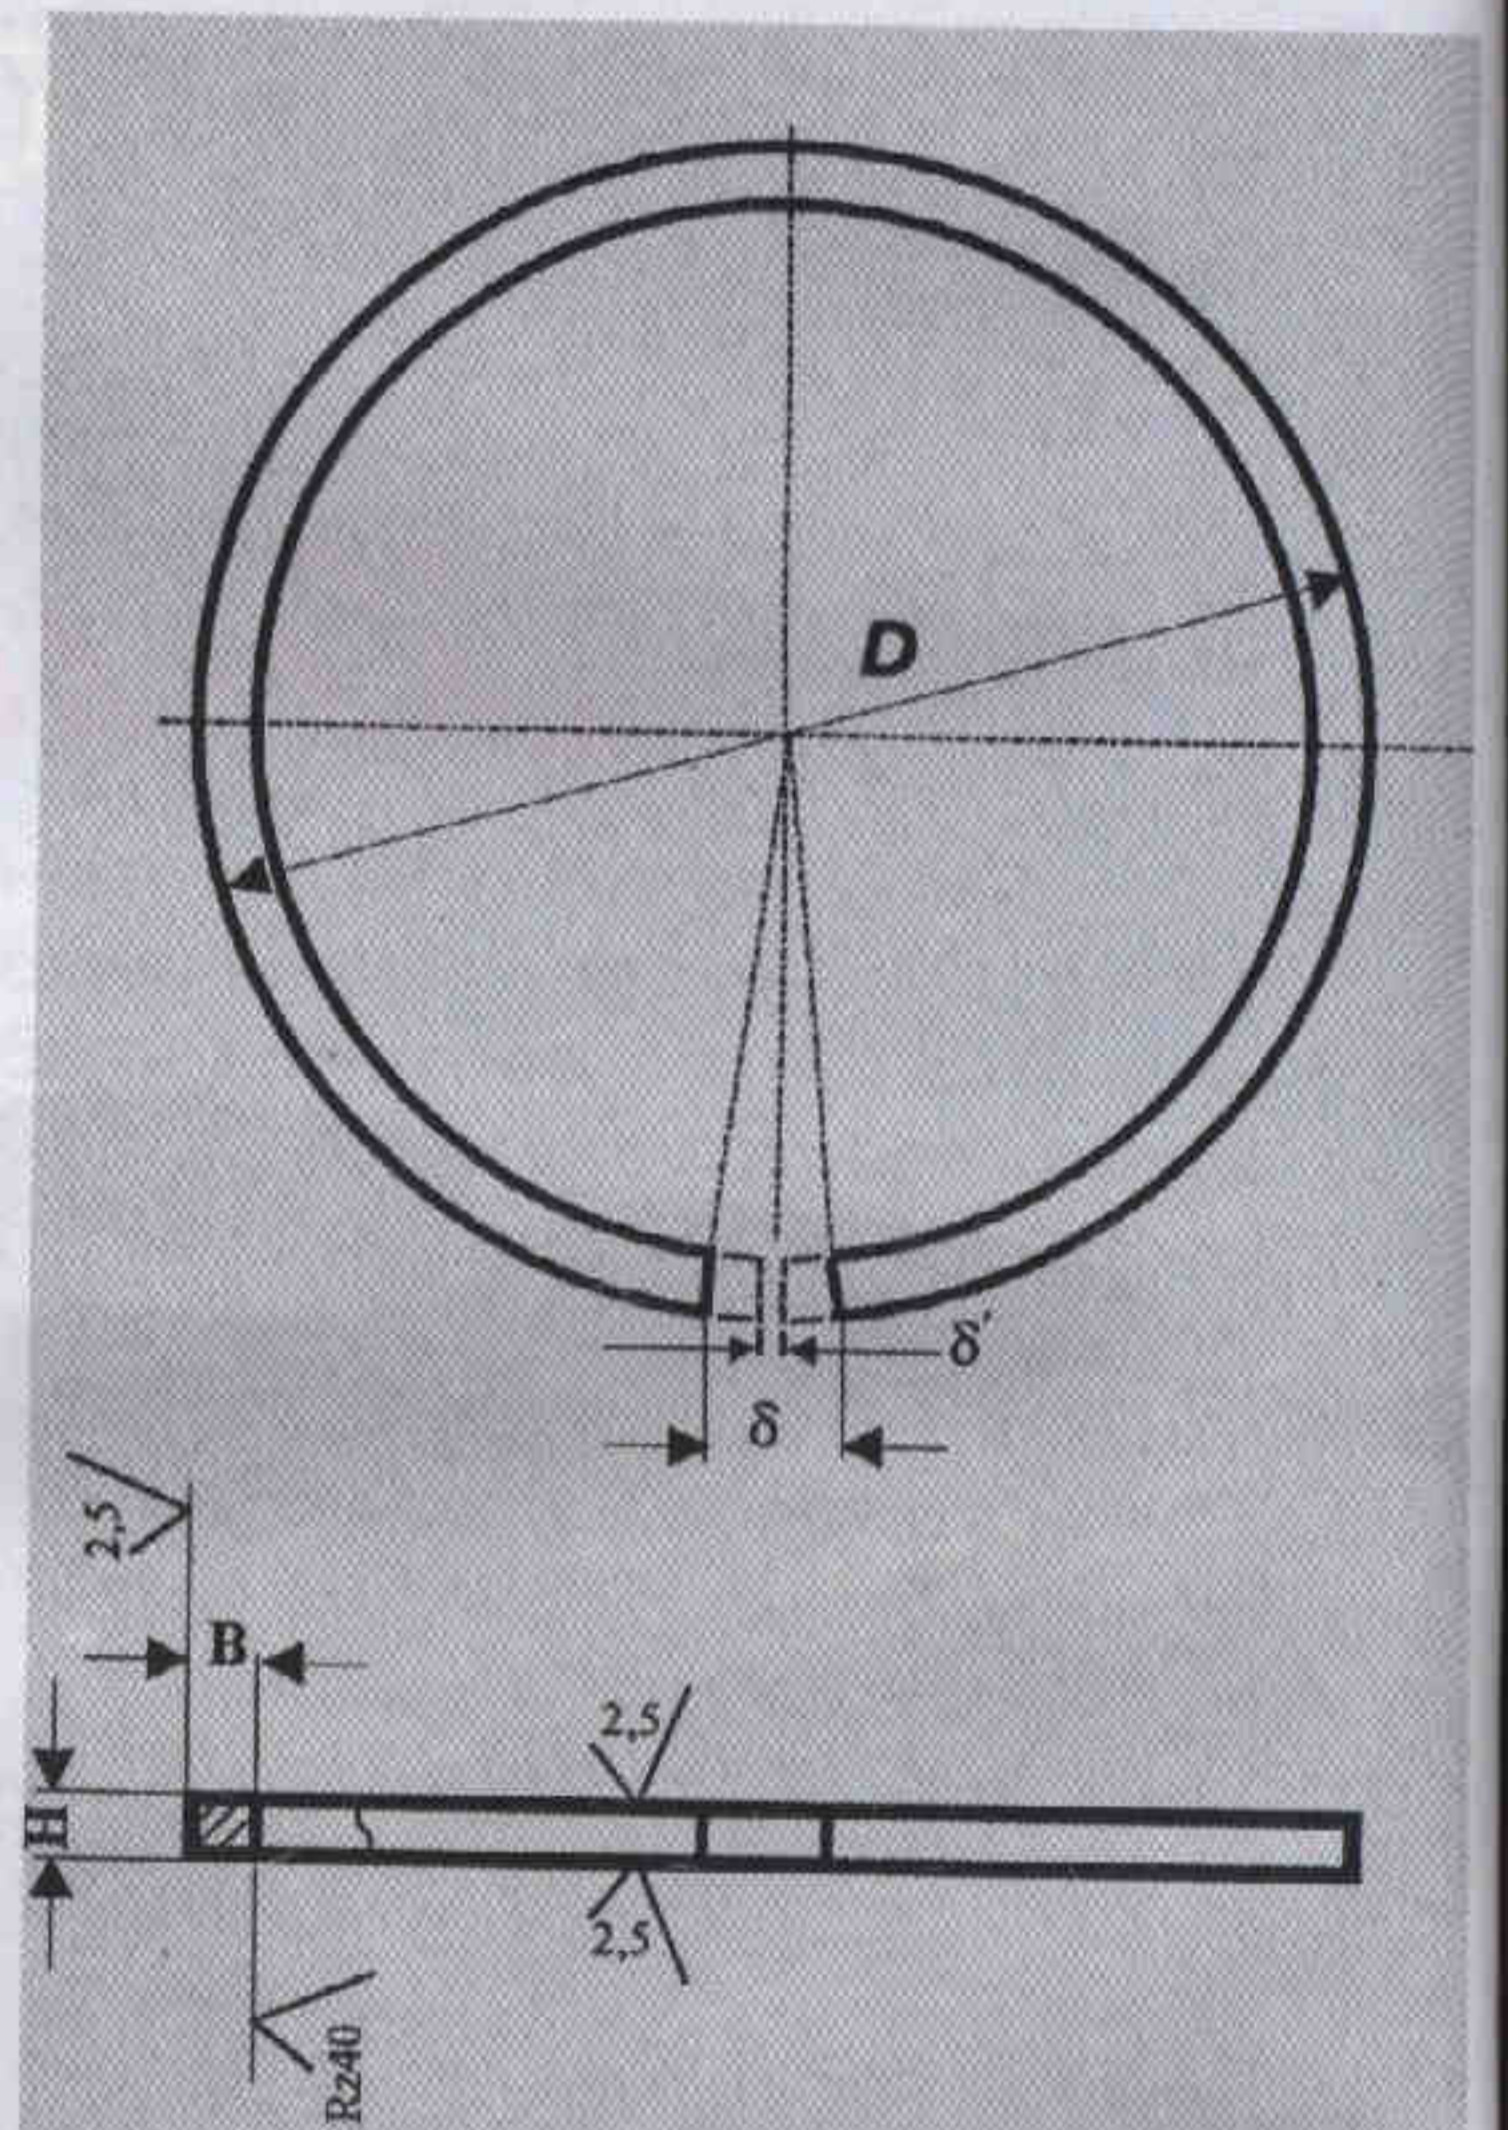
Металлокерамические уплотнительные кольца для холодильных поршневых компрессоров
